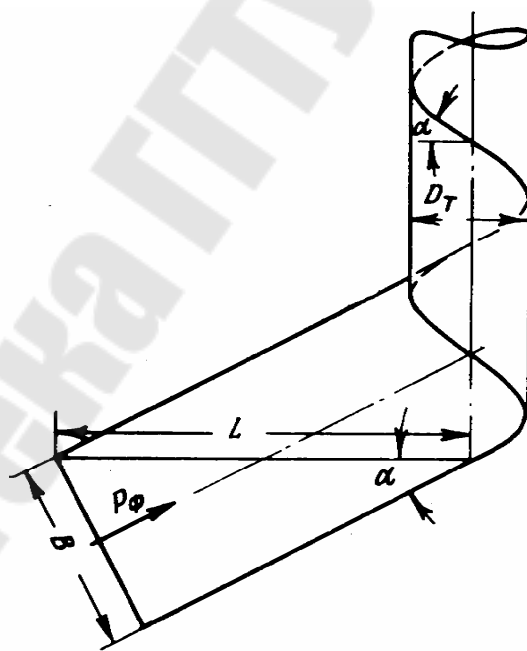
Схема формовки трубной заготовки при спиральной сварке трубы
